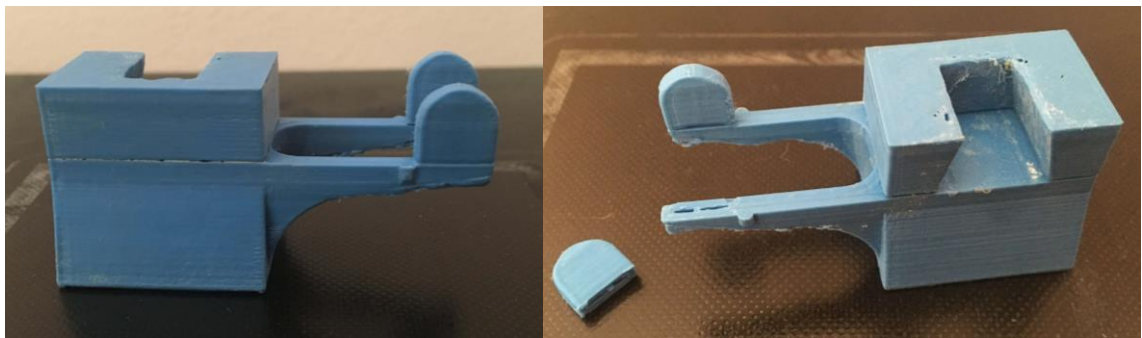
A la izquierda: grieta a través del plano horizontal de las palancas. A la derecha: fractura causada por la grieta.
